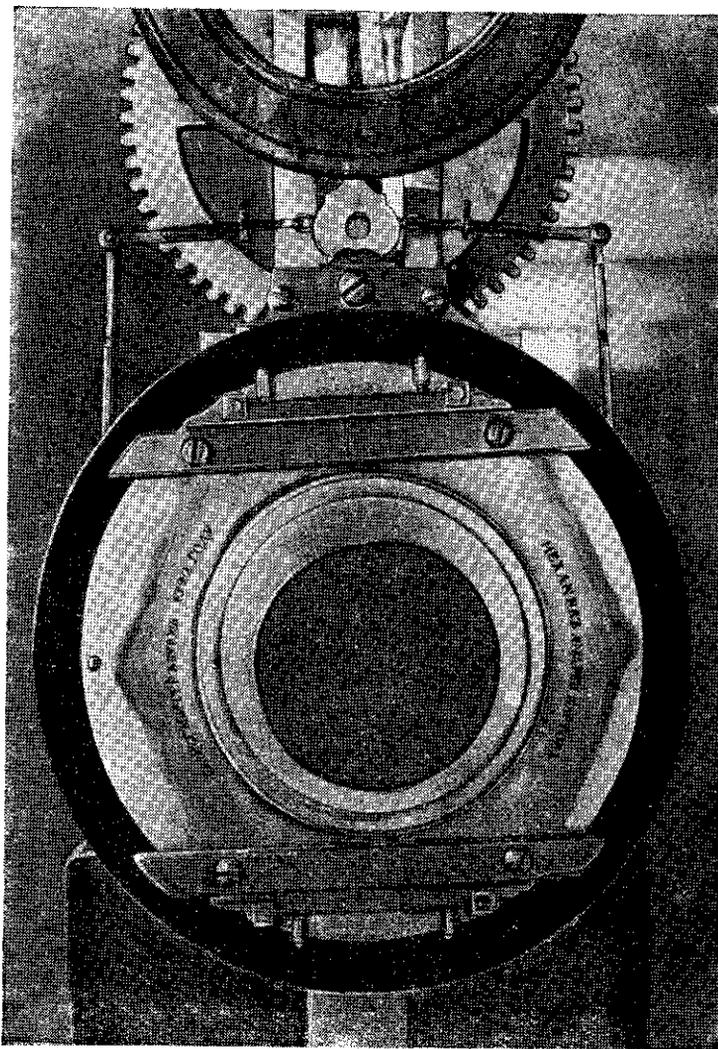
Узел механизма передней бабки с патроном-планшайбой в токарно-овальерном станке Нартова 1722 г.
